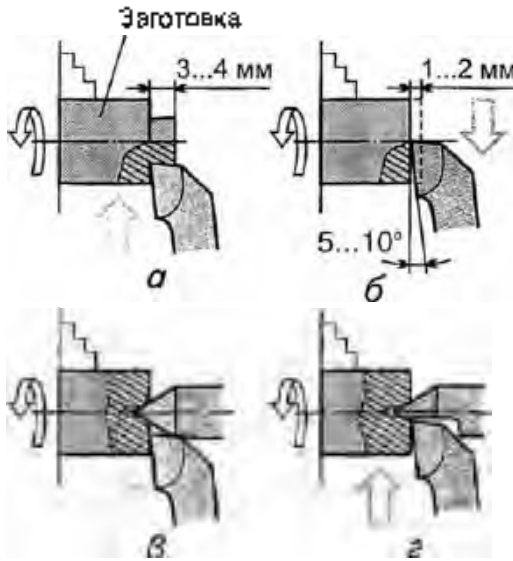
ПІДРІЗУВАННЯ ТОРЦЯ ПОПЕРЕЧНОЮ ПОДАЧЕЮ УПОРНОГО РІЗЦЯ:
